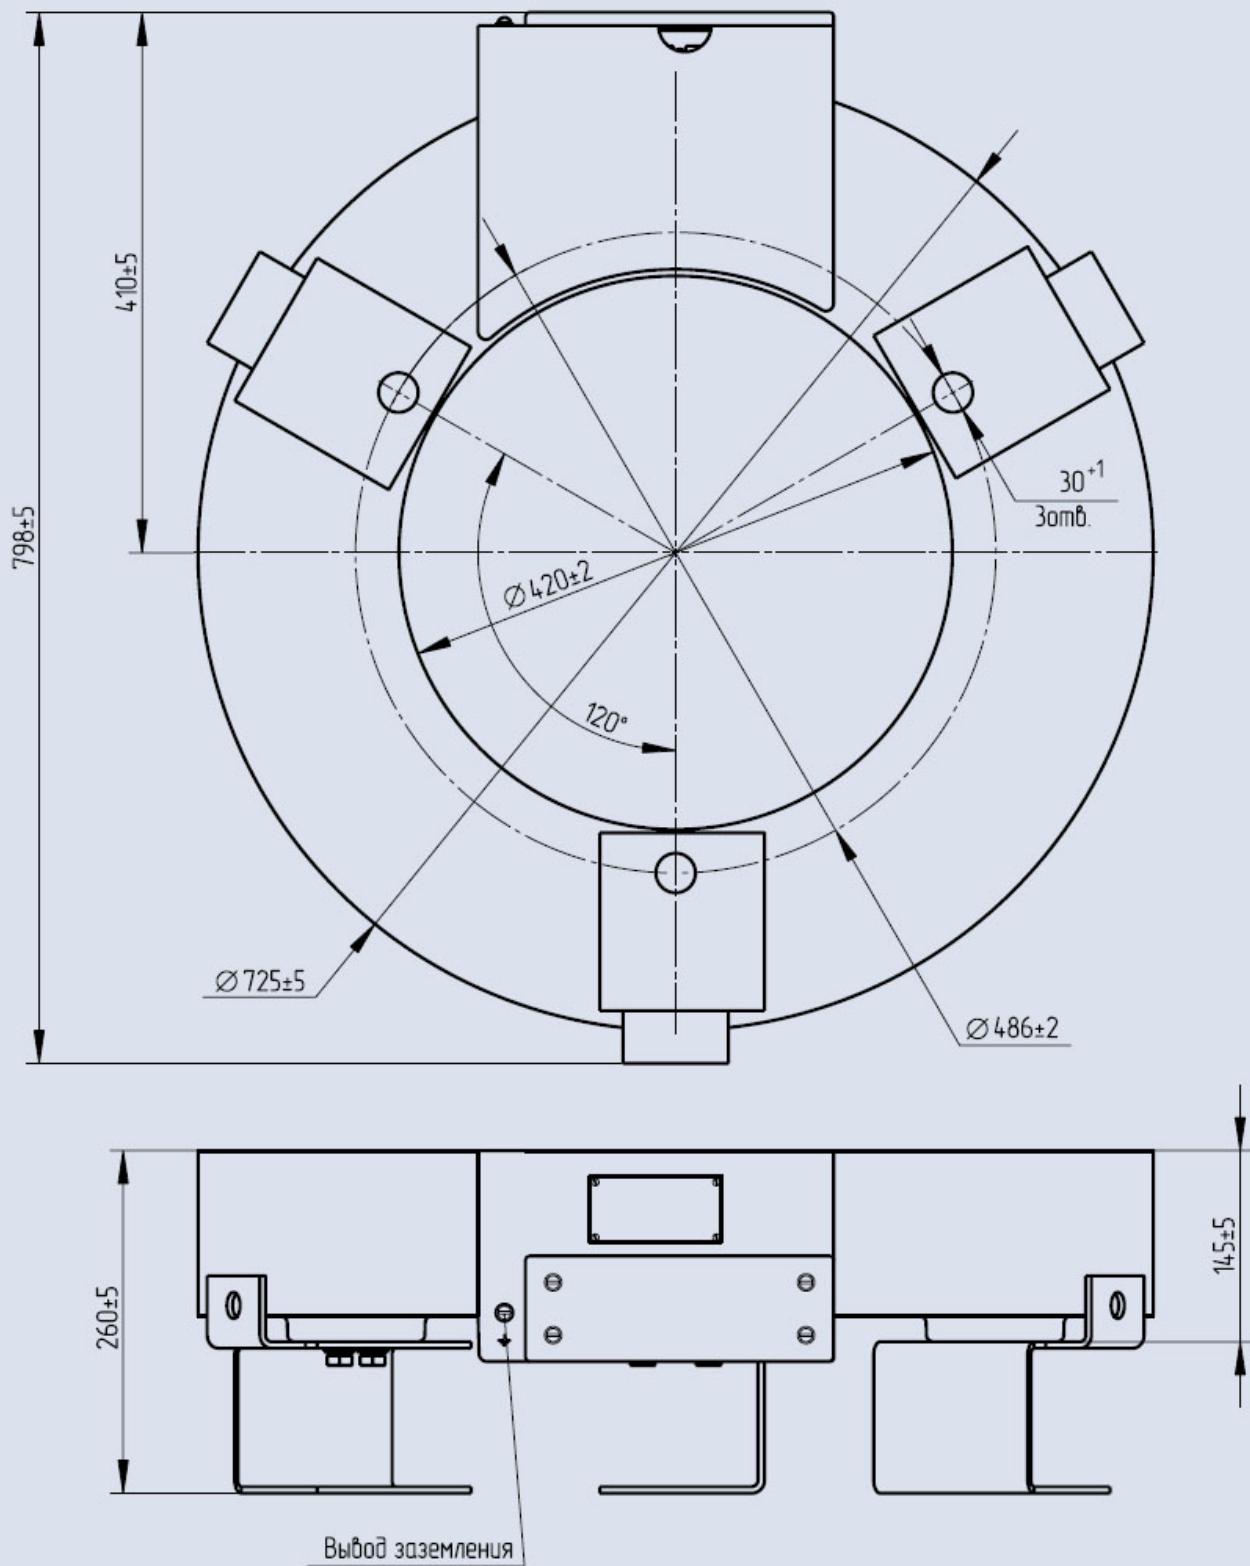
Габаритные, установочные и присоединительные размеры трансформатора ТВ-110-IX-3. Масса 125 кг
